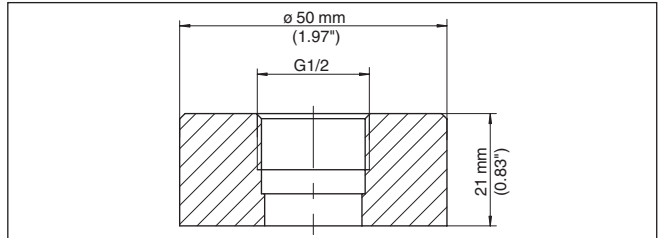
Maße Einschweißstutzen G½ B (ISO 228-1) Behälter - VEGABAR 17
